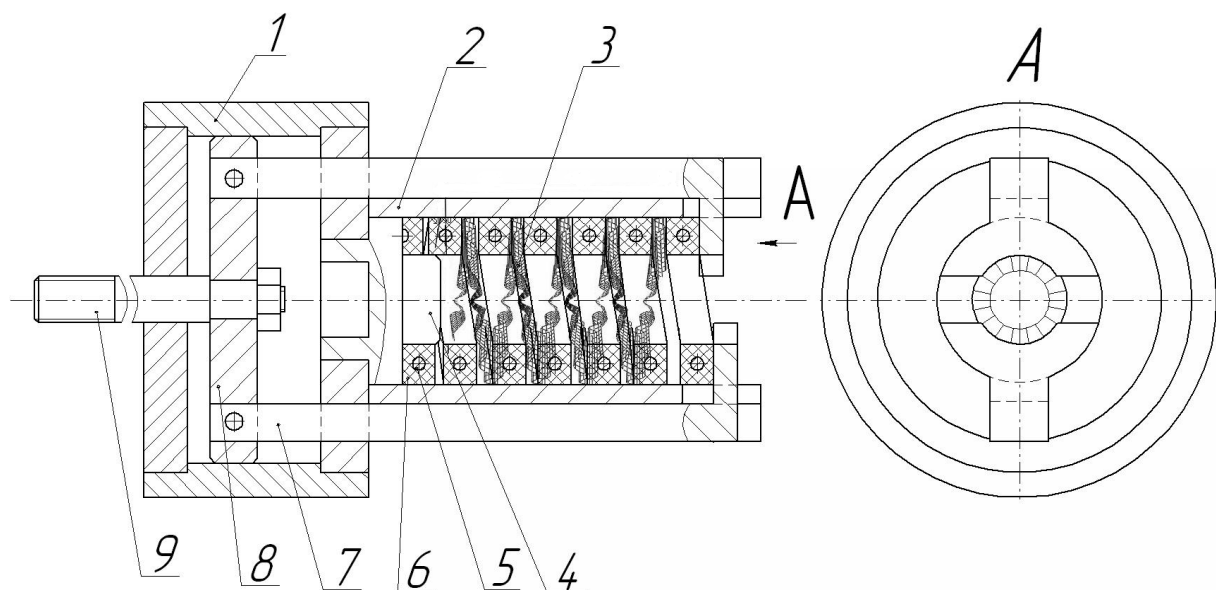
Пристрій для розточування внутрішнього діаметра ГГЗ
